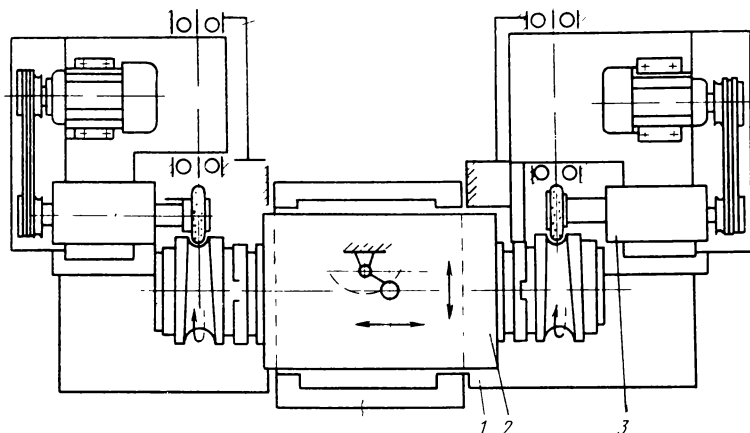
Станок для шлифования ручьев калибров станков модели ЛЗ 250
